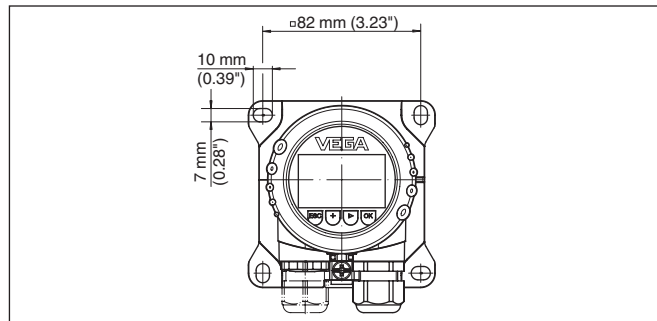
Dimensioni dei fori nel VEGADIS 81 per il montaggio a parete
